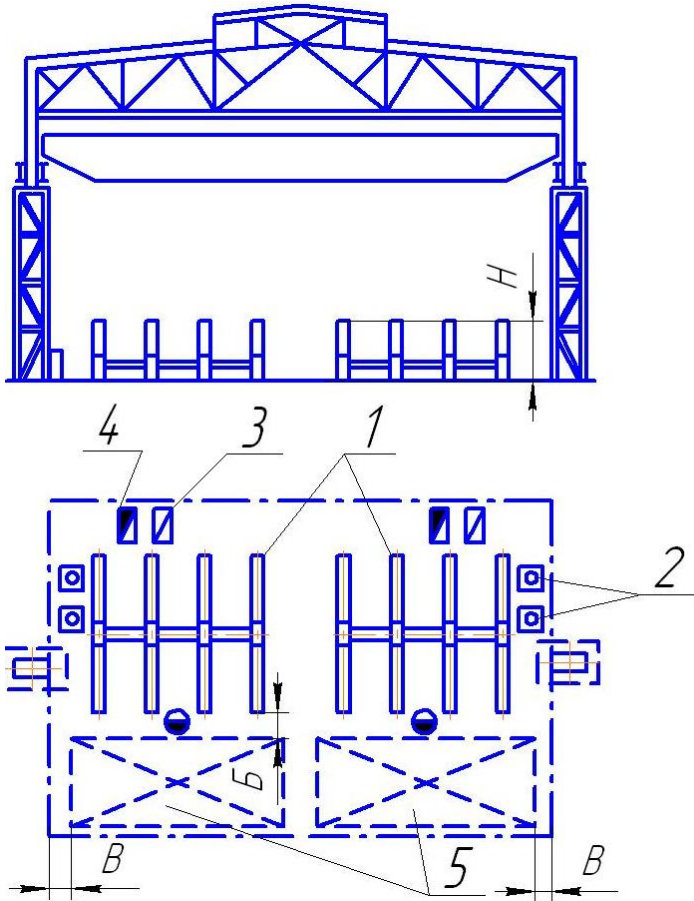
Размещение участка для сварки конструкций с использованием станда для сварки:
